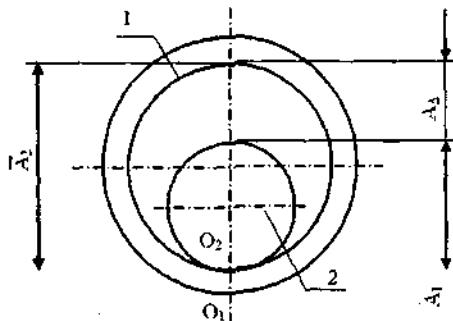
Замыкающий размер в сборочной размерной цепи:
